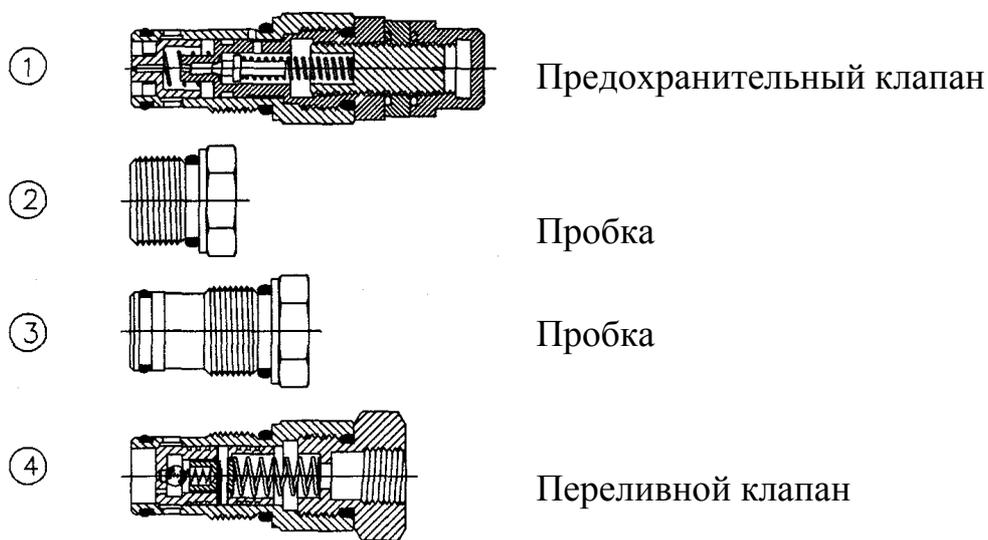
Примерные конструкции клапанов, пробки и заглушки
